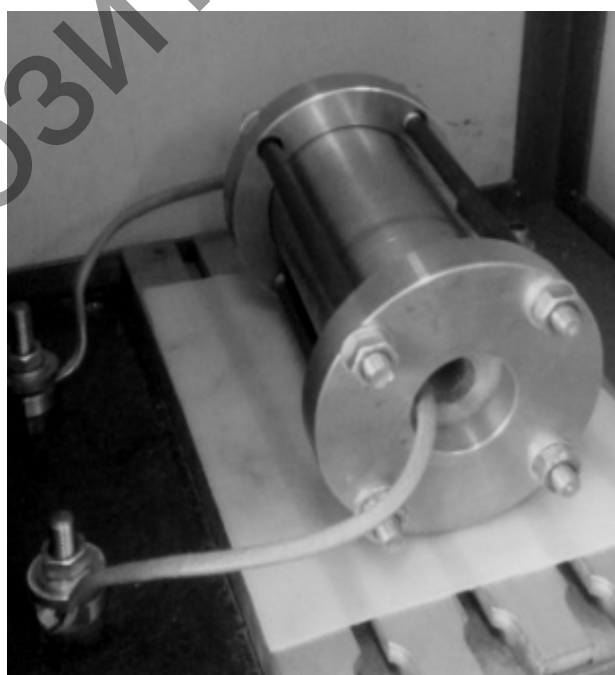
Индуктор цилиндрический для МИО цилиндрических образцов и изделий
